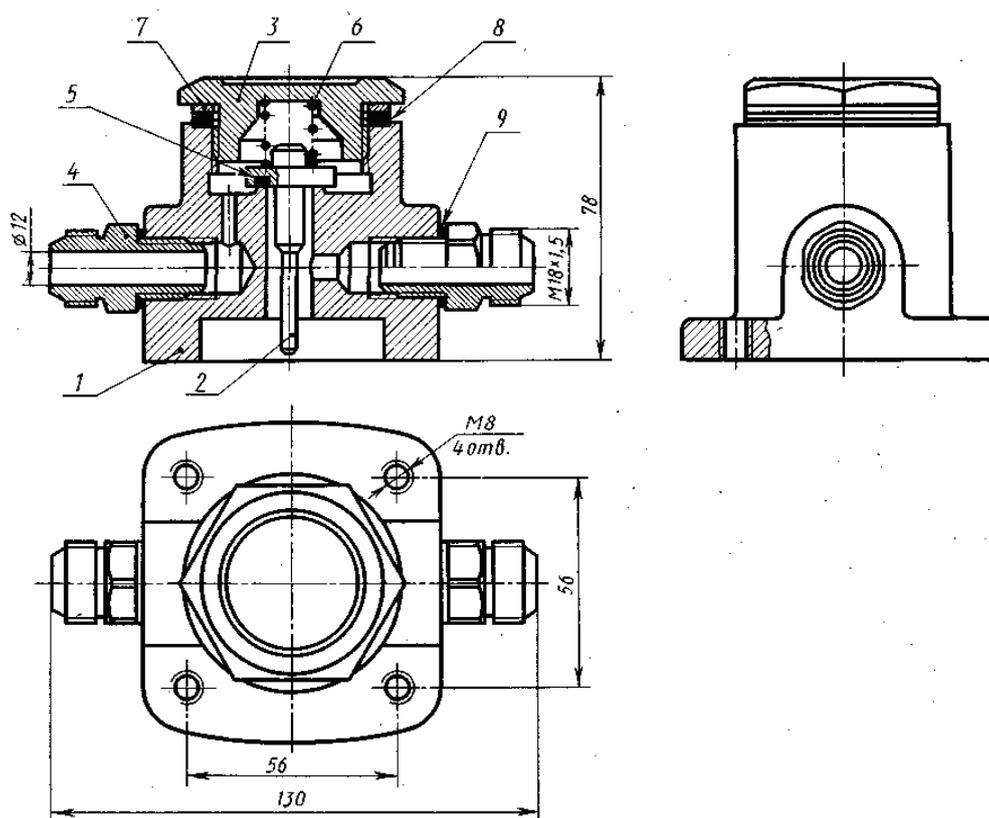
Сборочный чертеж сборочной единицы Клапан предохранительный
